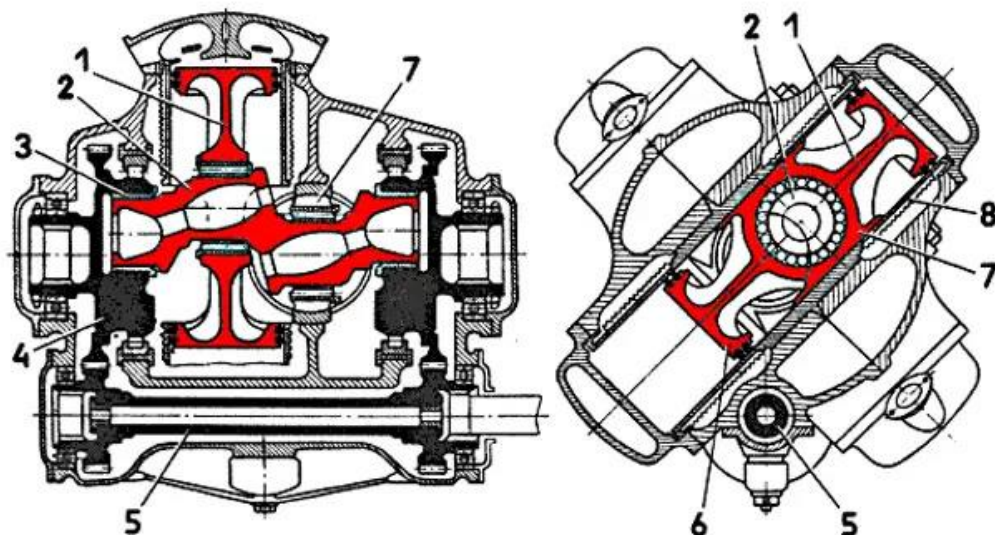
Компоновка бесшатунного двигателя одинарного действия: 1 – поршневой шток; 2 – коленчатый вал; 3 – подшипник кривошипа; 4 – кривошип; 5 – вал отбора мощности; 6 – поршень; 7 – ползун штока; 8 – цилиндр
